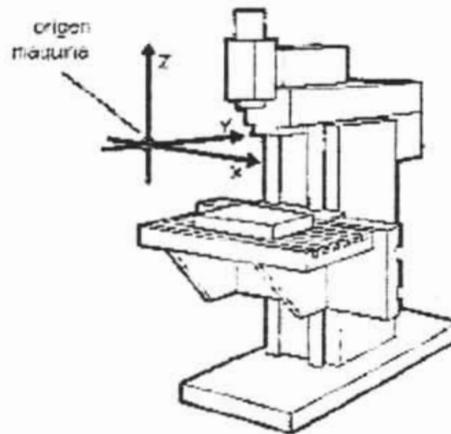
Posición del origen máquina en fresadoras de CNC DYNA 4M
